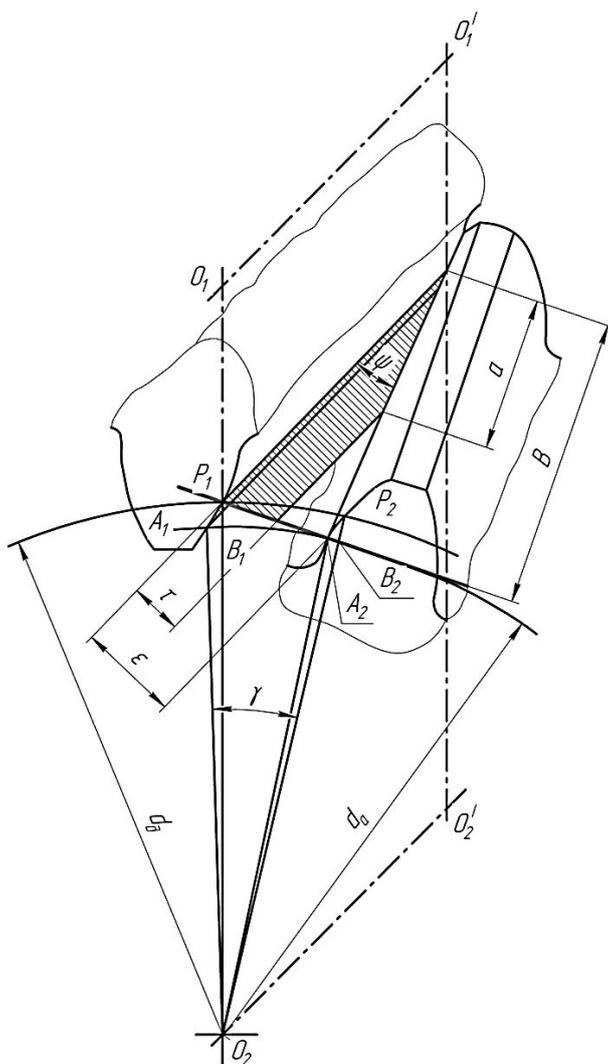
Схема сопряжения боковых поверхностей зубьев цилиндрической передачи и образования угла их неприлегания
